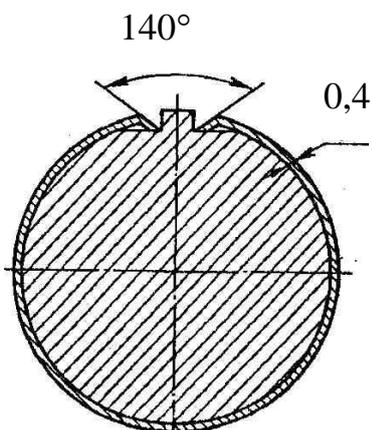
Восстановление шеек коленчатого вала пластинированием
